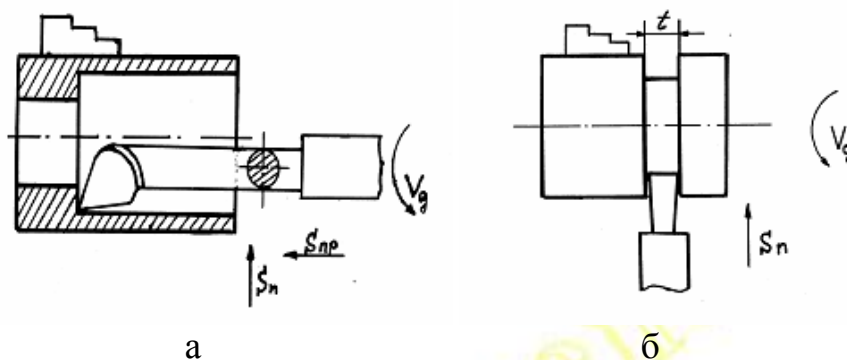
Расточной упорный резец (а) и отрезной резец (б)
